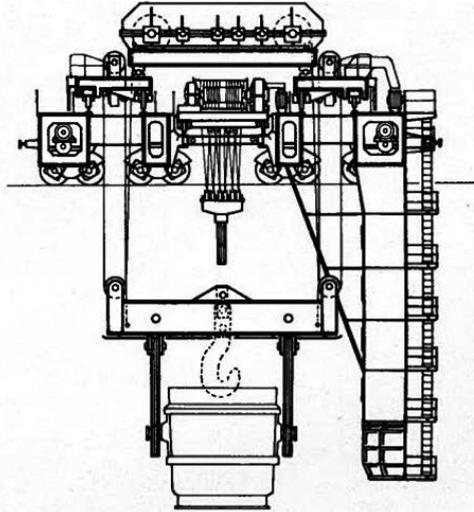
Grúa de colada de 350 Tm. con carro auxiliar de 80/20 Tm. y 22,5 m. de luz.
